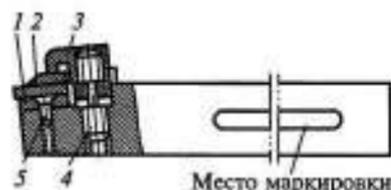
Конструкция резца с минералокерамической пластиной: 1 — опорная пластина из твердого сплава; 2 — режущая пластина из минералокерамики; 3 — прихват; 4 — дифференциальный винт; 5 — винт
